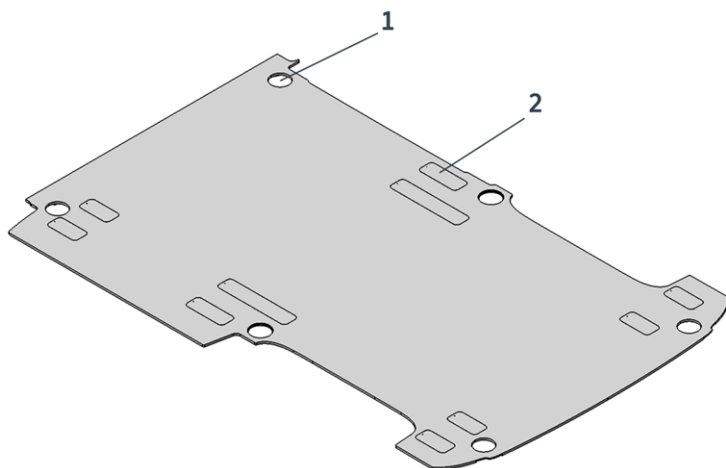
plancher universel (5BM), sur la figure ci-contre : Transporter court empattement avec porte coulissante droite
